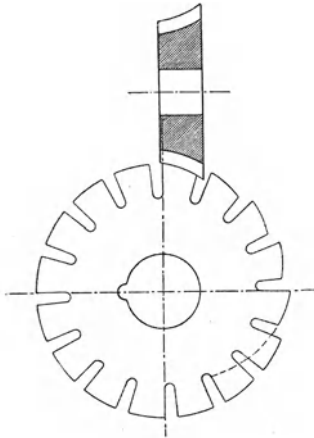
Das Fräsen der Zähne anstatt des Hinterdrehens.
